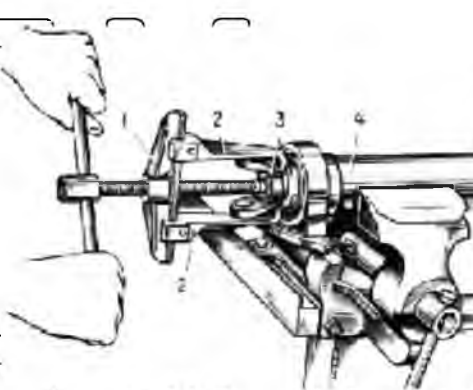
Зняття вилки з переднього карданного вала: 1 - знімач А.40005/1/5; 2 - важелі знімача; 3 - вилка переднього карданного вала; 4 - передній карданний
